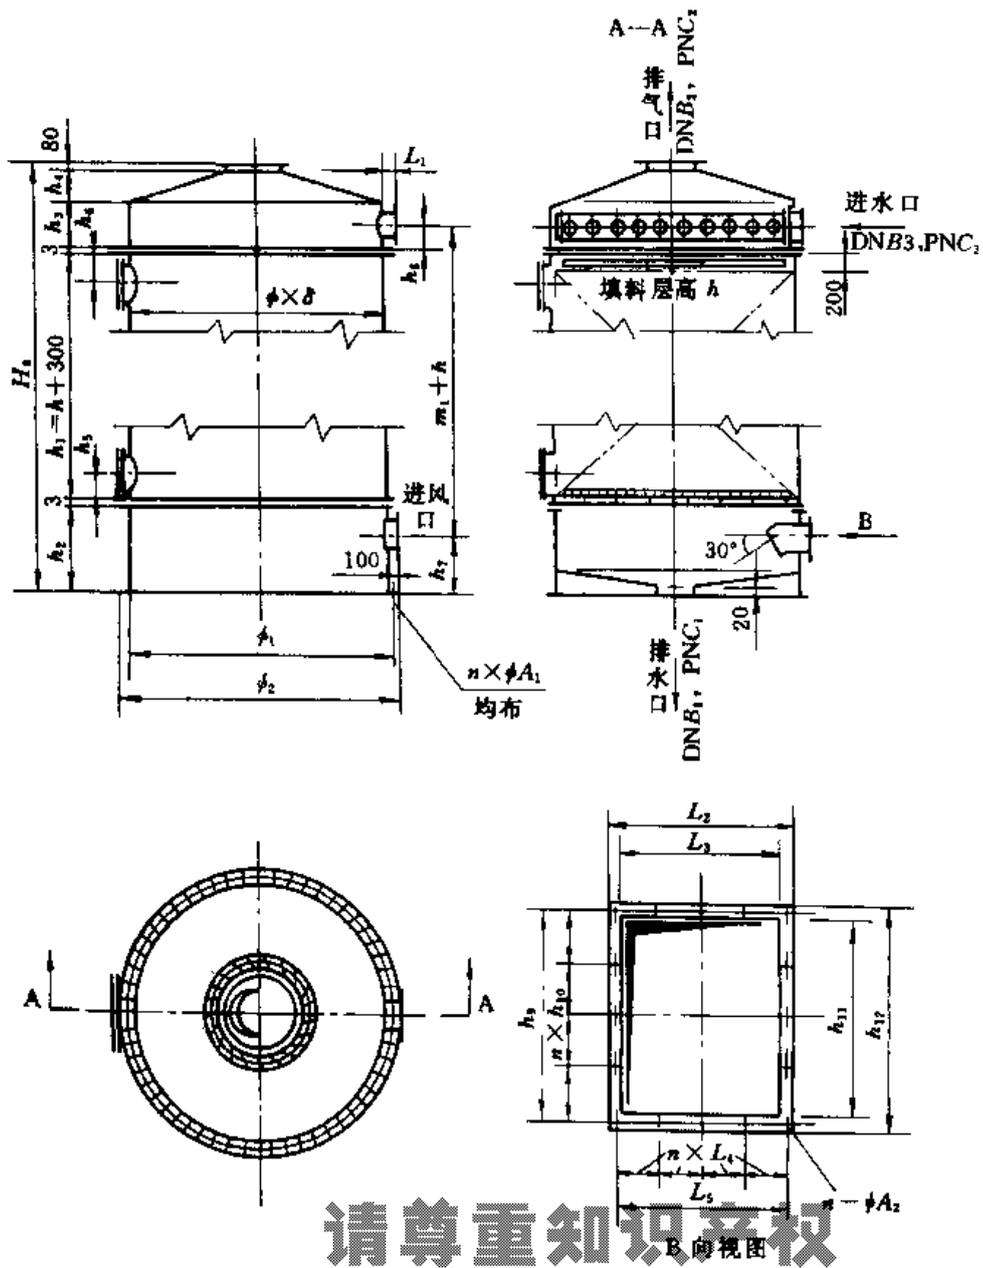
DN1000~DN3200 HB·Ch 除碳器外形尺寸
